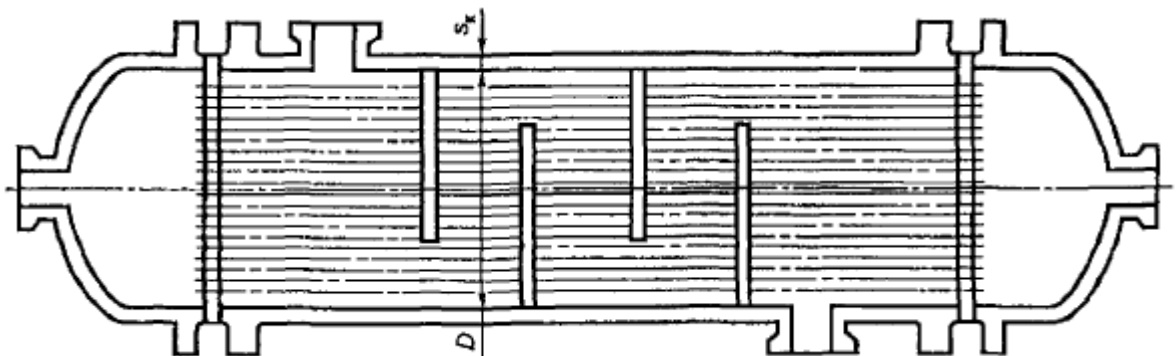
Схема аппарата с неподвижными трубными решетками
